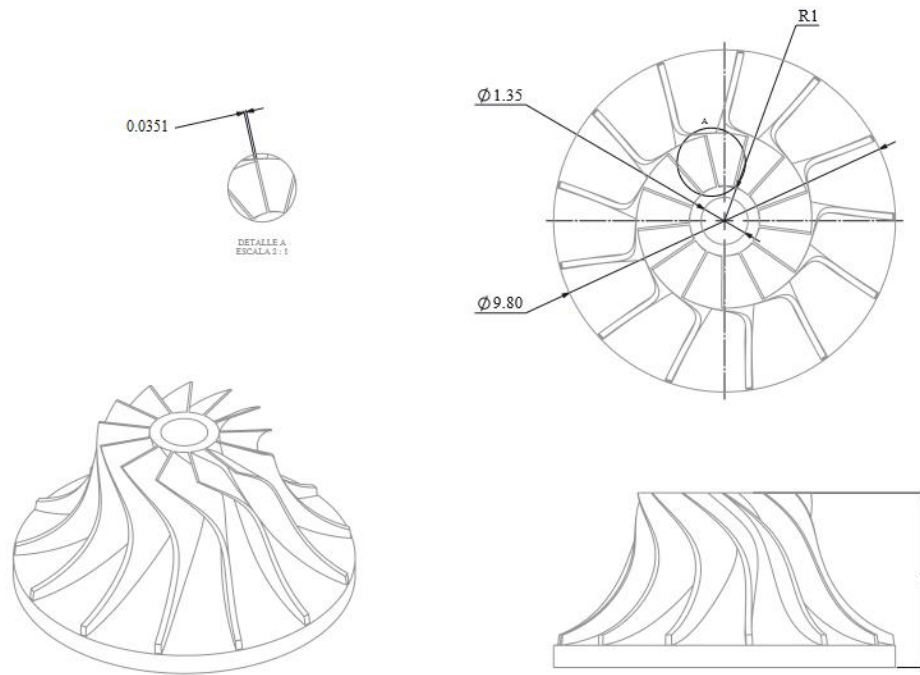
CAD con dimensiones (cm) del rotor 13 álabes.
